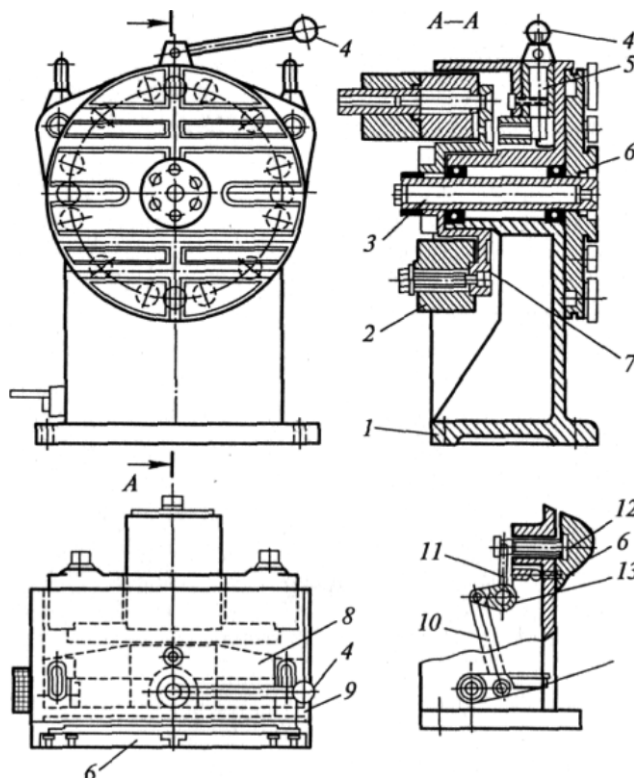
Одноопорна поворотна стійка з пневмогідравлічним приводом: 1 – корпус; 2 – вантаж; 3 – шпindelь; 4 – рукоятка; 5 – ексцентриковий валик; 6 – планшайба; 7 – диск; 8 – планка; 9 – палець; 10, 11, 13 – важелі; 12 – фіксатор; 14 – педаль
